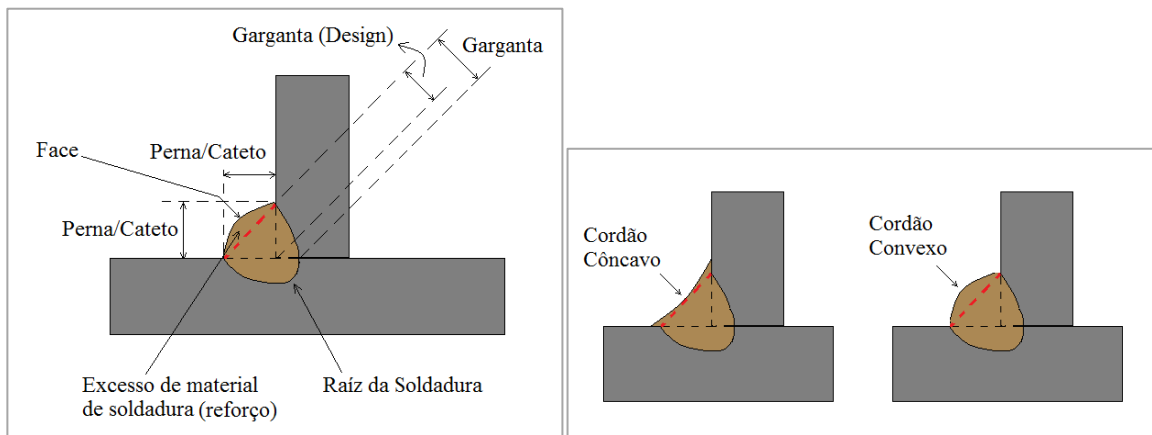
Principal nomenclatura de uma soldadura (à esquerda) e concavidade (à direita) - [10] Imagem adaptada
